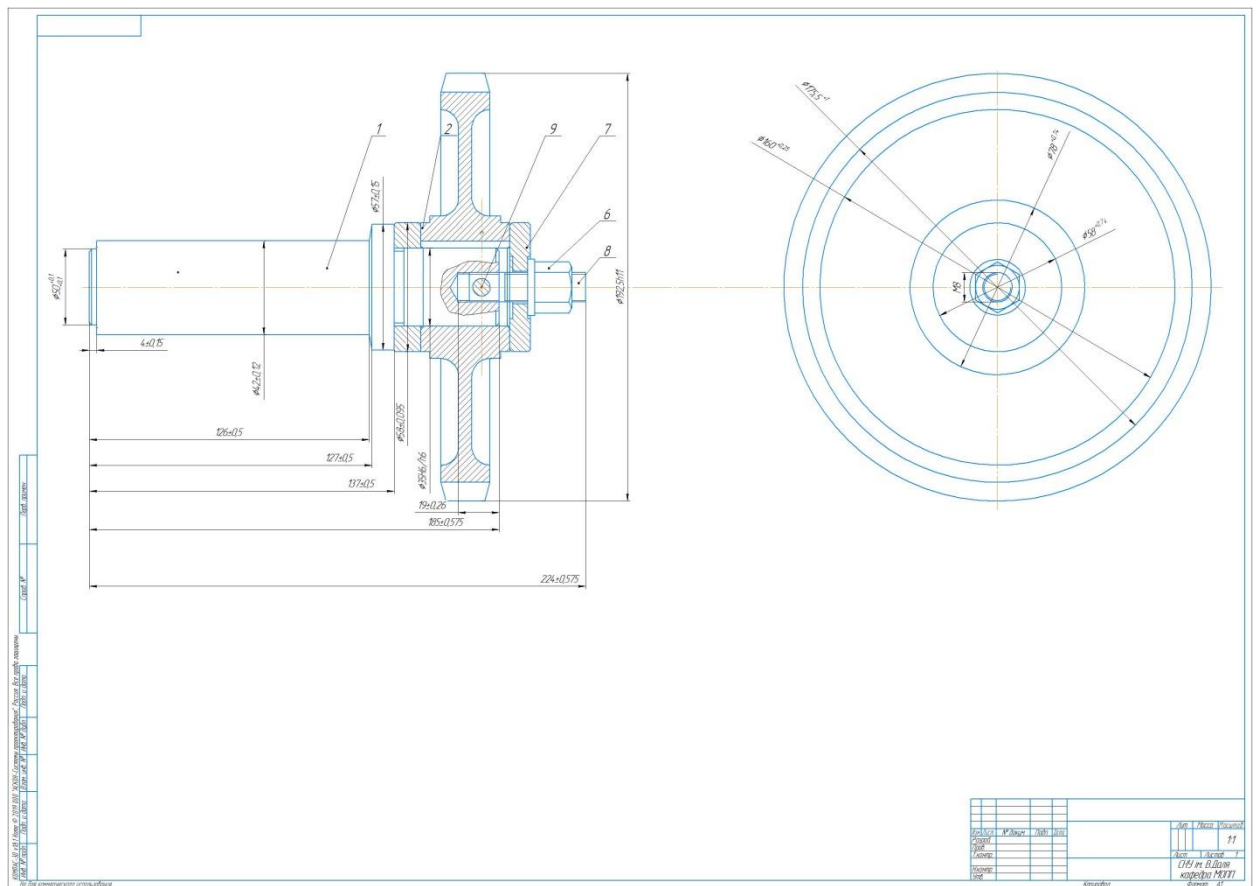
Конструкція оправки для встановлення деталі по отвору при чистовій обробці поверхні 7, на якій у подальшому нарізуються зуби
